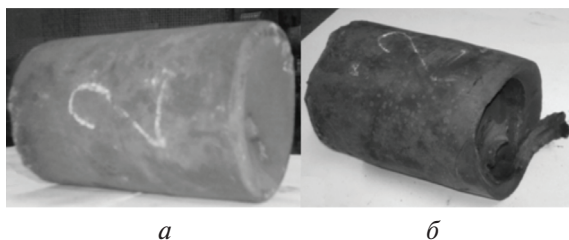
Фото задних концов обжатой заготовки и гильзы (заготовка с выпуклым торцом размером  $L = 25 \pm 5$  мм с  $R = 180$  мм)
